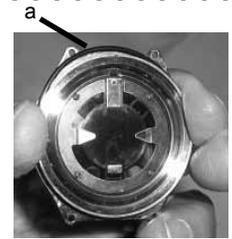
PINCEMENT DU JOINT TORIQUE DU COUVERCLE
